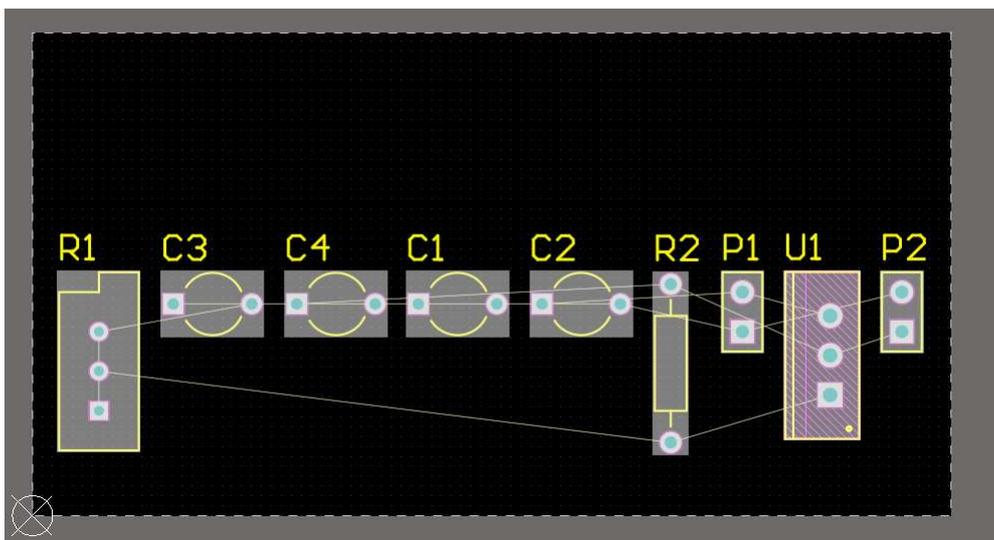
Bauteile ohne Rahmen auf PCB ziehen
